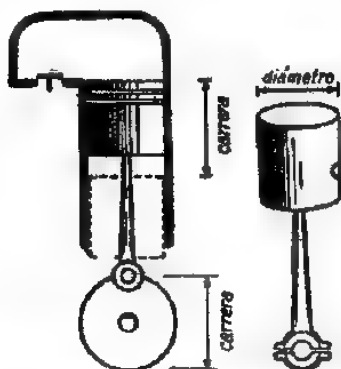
Indicación de las dimensiones principales a tener en cuenta para el cálculo de la cilindrada de un motor.
